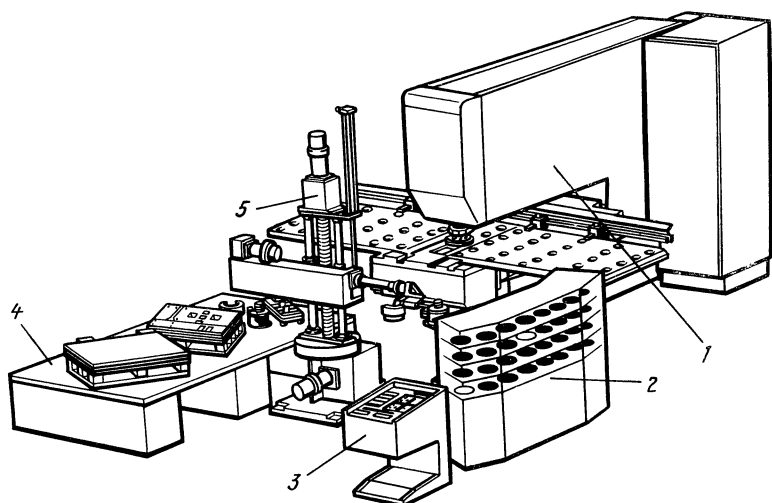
ГПМ для пробивки и высечки листового металла:
